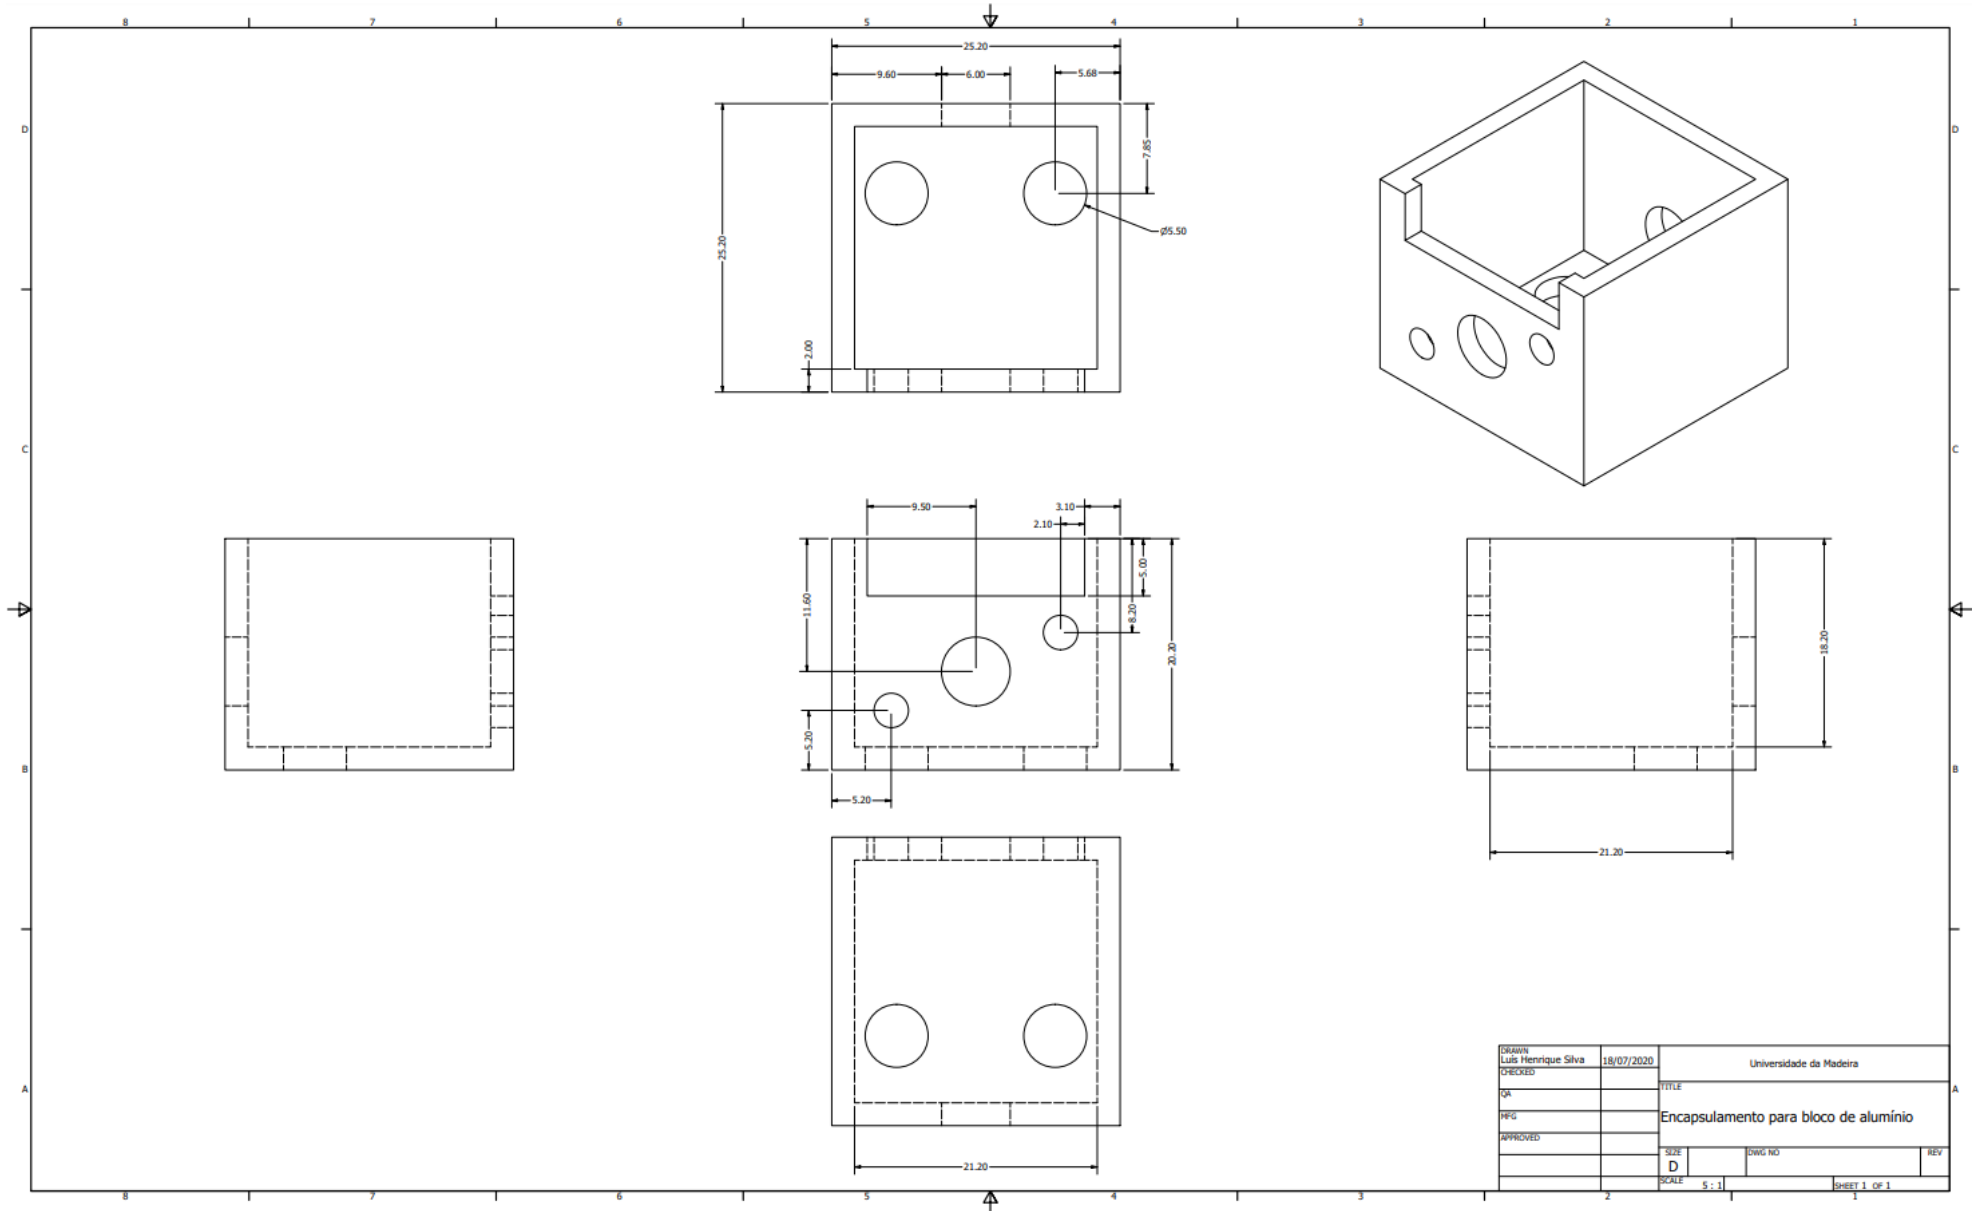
Desenho técnico do encapsulamento criado para o bloco de alumínio
